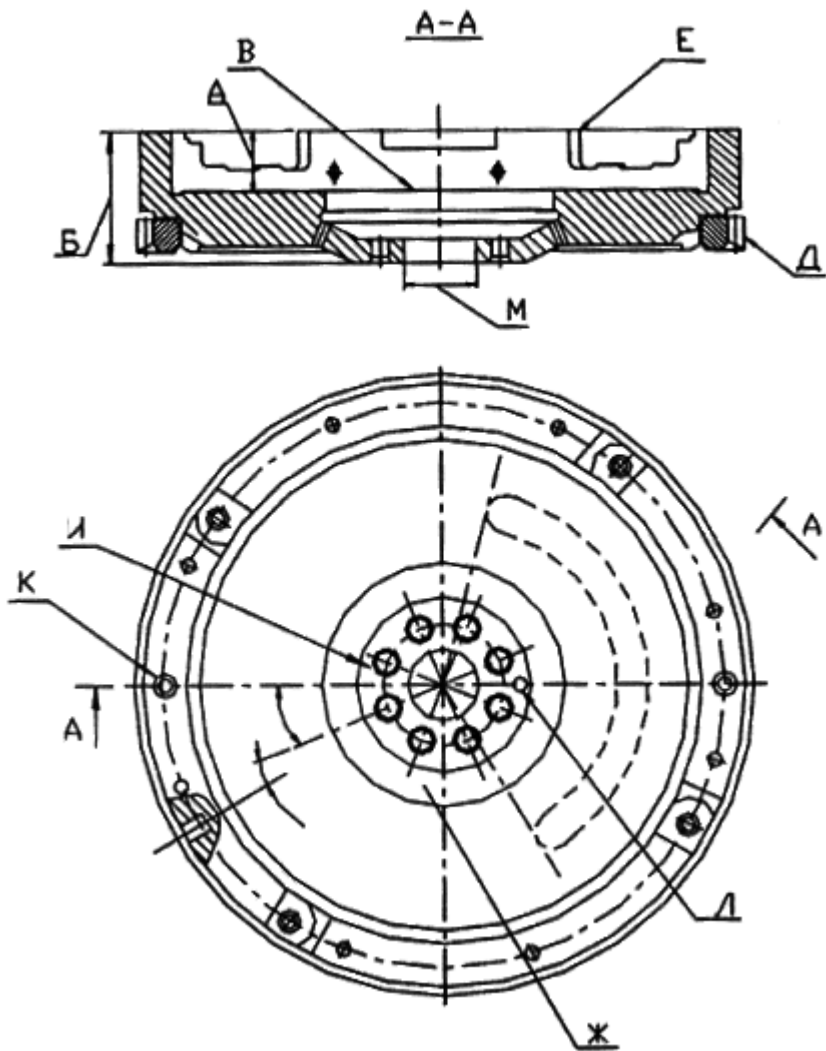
Маховик коленчатого вала двигателя КамАЗ-740
